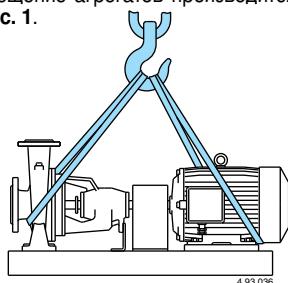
Строповка канатами для поднятия двигатель-насосного агрегата.
